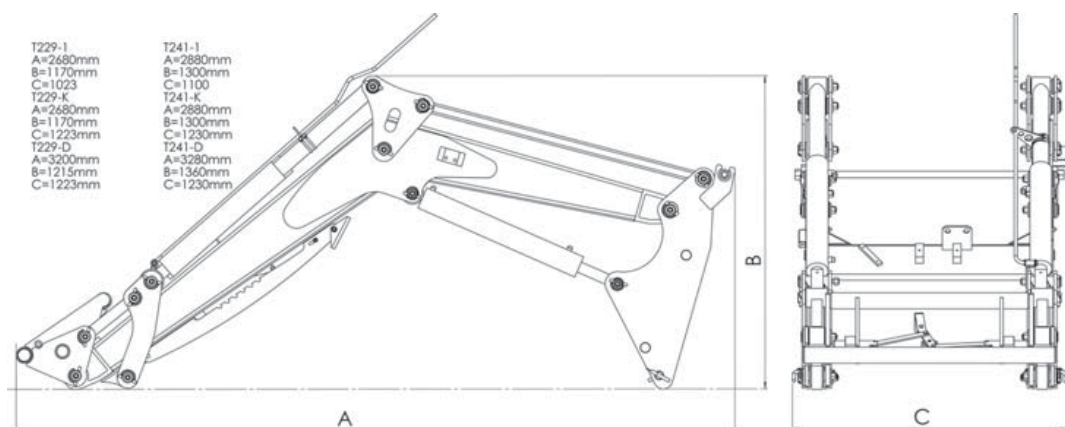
Размеры погрузчика, подготовленного для транспортировки
